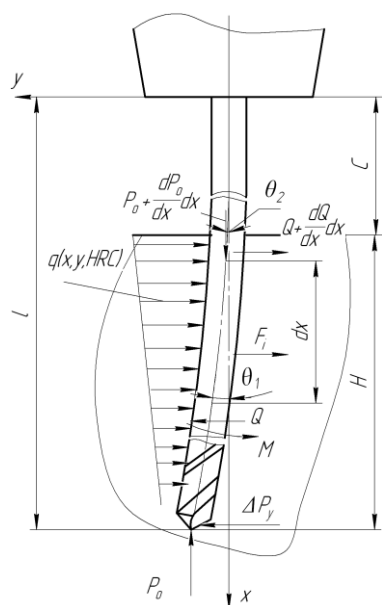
Розрахункова схема для визначення коливань свердла в процесі свердління отвору
